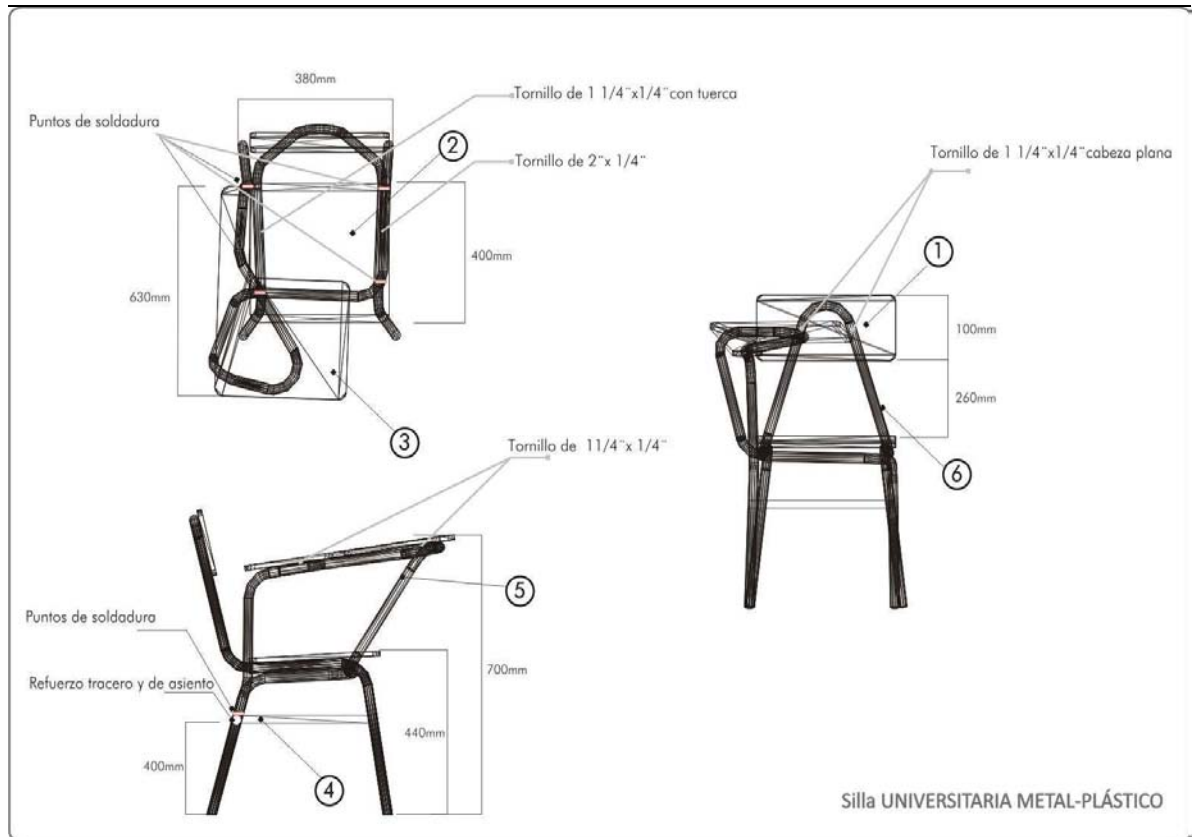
Despiece de las partes de una silla universitaria Metal Plástica
